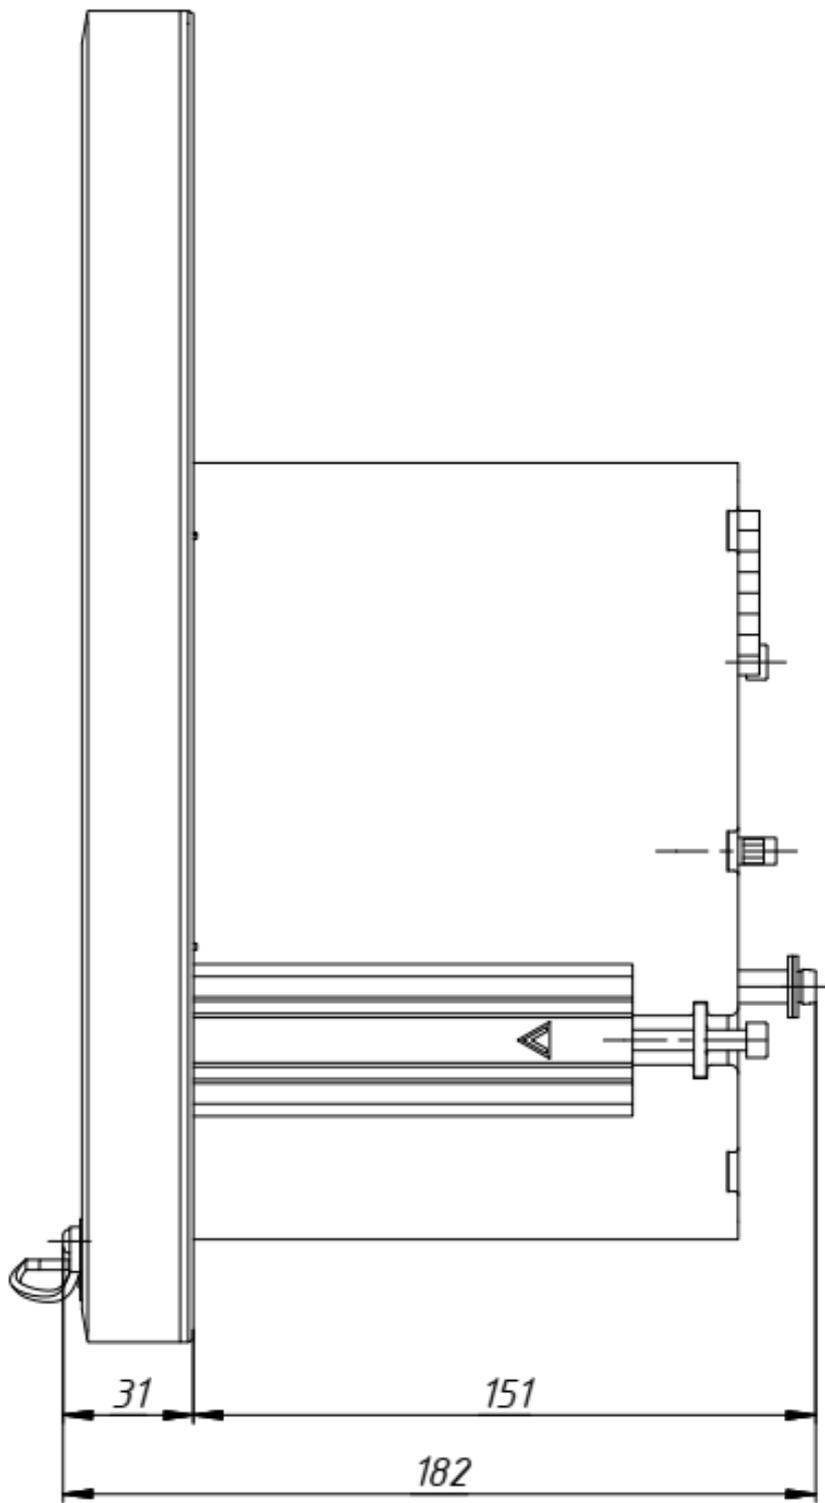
Габаритный чертёж прибора в исполнении Ф1772–2, вид сбоку
